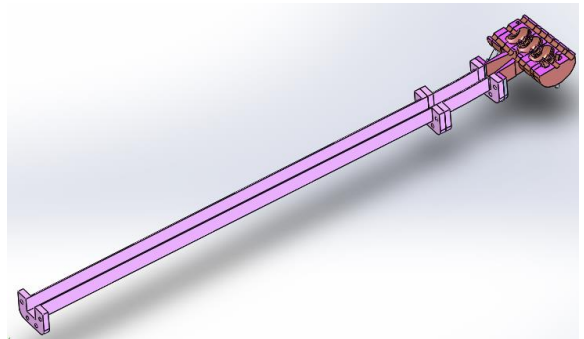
Vista de la secció en planta de tota l'estructura d'acceleració.
